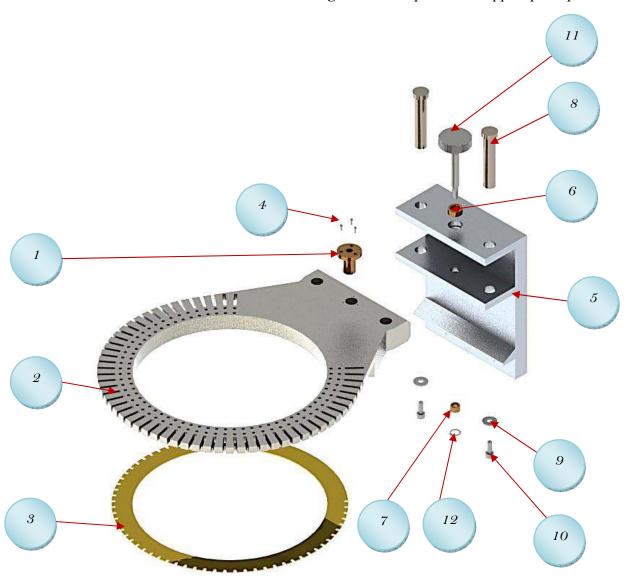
Vue éclatée de Dispositif de support porte pointes
